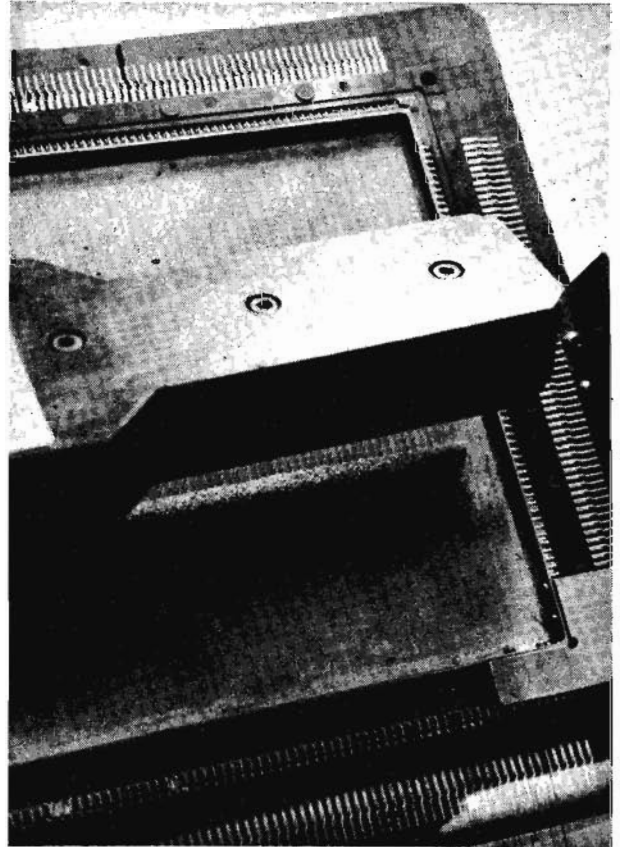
La mémoire à aiguilles est fabriquée entièrement automatiquement. L'utilisation d'un champ magnétique permet à des milliers d'aiguilles de se dresser sur la pointe et de « marcher » sur le plan de mémoire. Les aiguilles viennent se planter au fur et à mesure dans chacun des trous du plan de mémoire. (Document NCR.)
